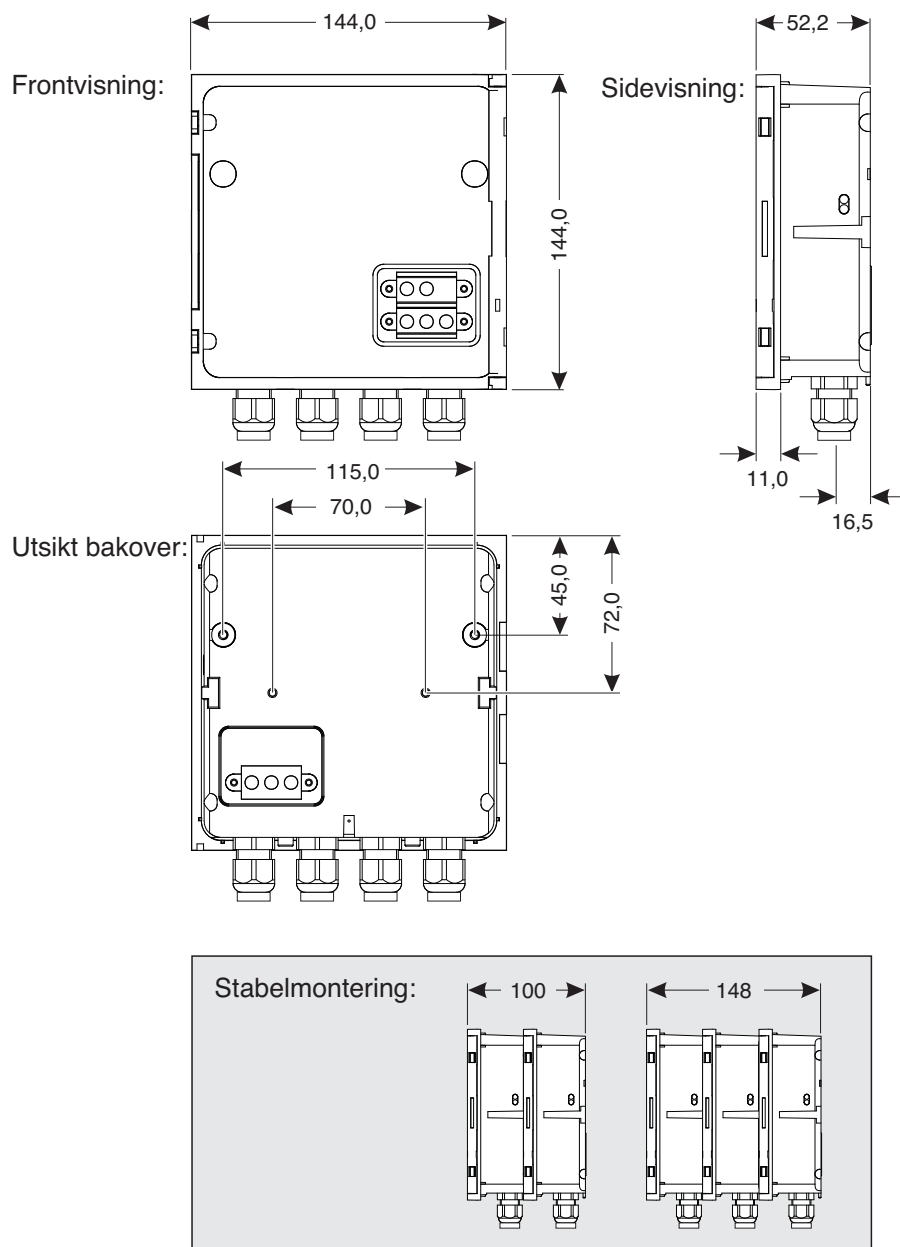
Dimensjonstegning av MIQ-modul (dimensjoner i mm)
